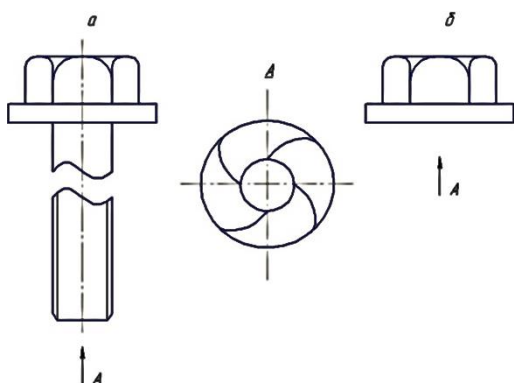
Детали резьбовых соединений [1]: а – болт, б – гайка
